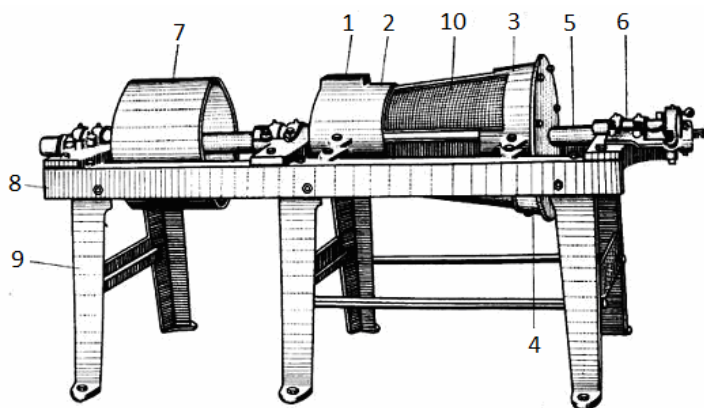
Degerminatorul de porumb model Beall Illinois: 1- gură alimentare; 2- carcasă; 3- sectorul de prelucrare finală; 4- gură evacuare produs; 5- axul rotorului; 6- lagăr; 7- roată antrenare; 8- batii; 9- picioare de sprijin.
